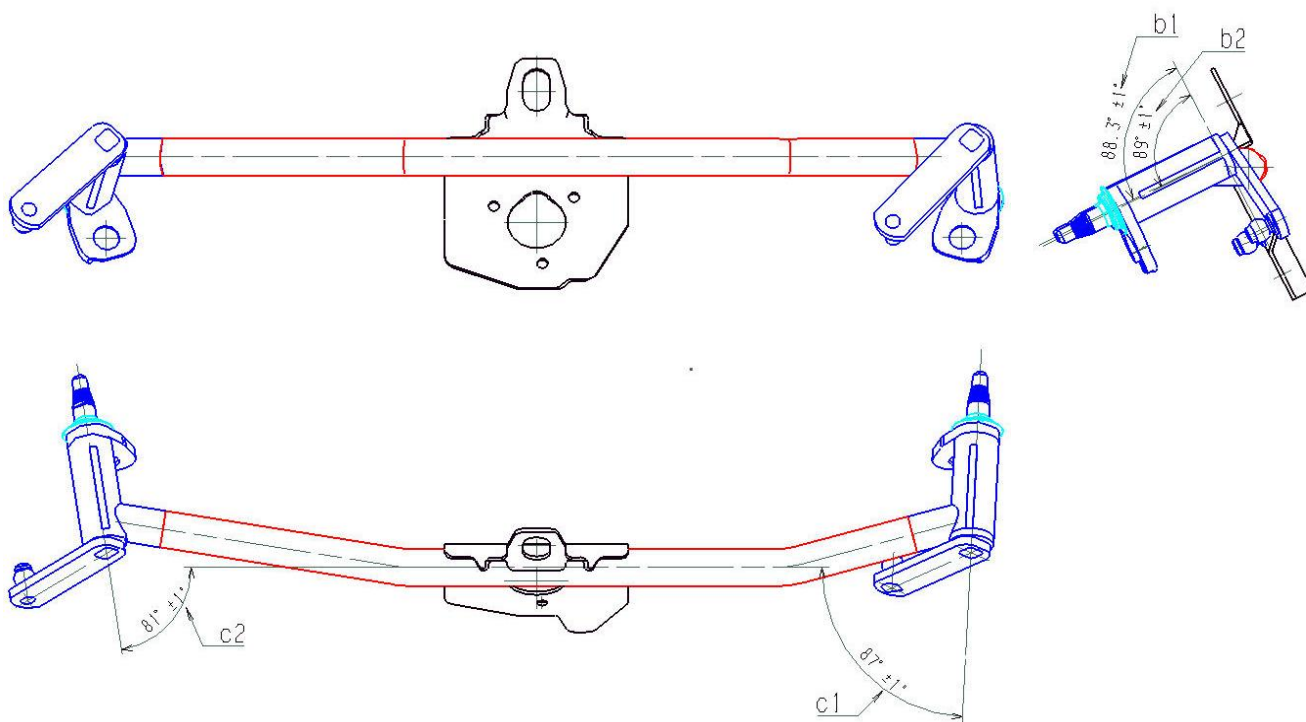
Natočení stěračové soupravy vlivem tolerance plechů – geometický součet tolerancí
